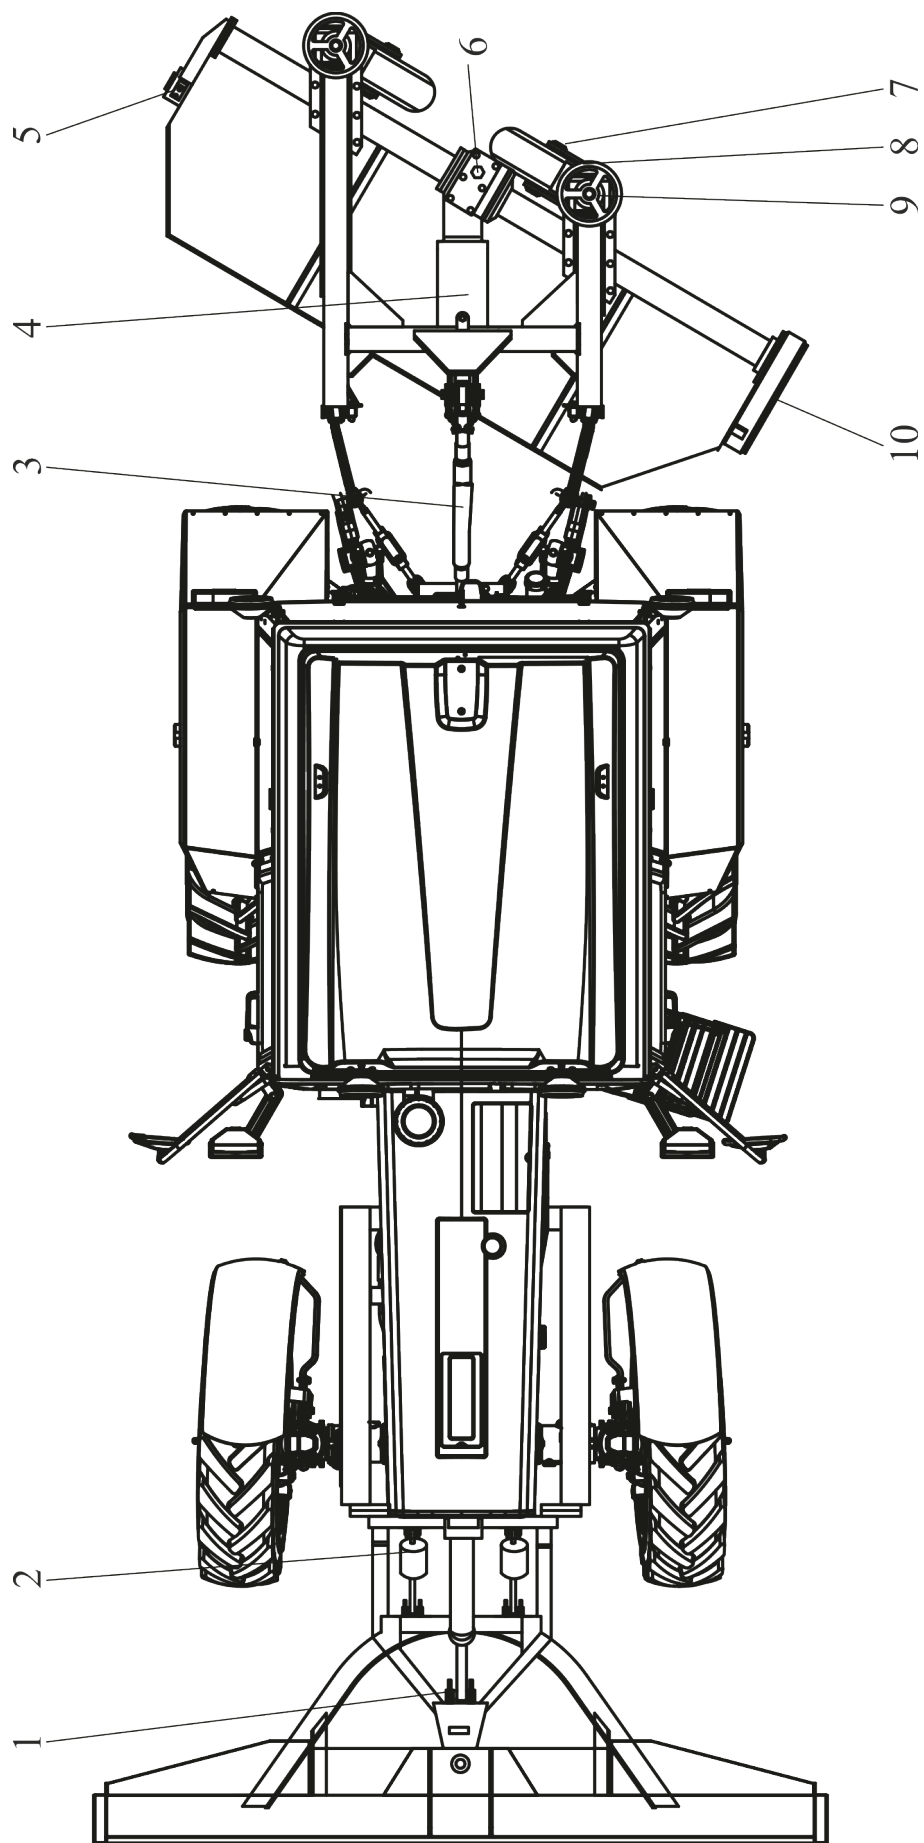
Схема смазки и заправки навесного оборудования
